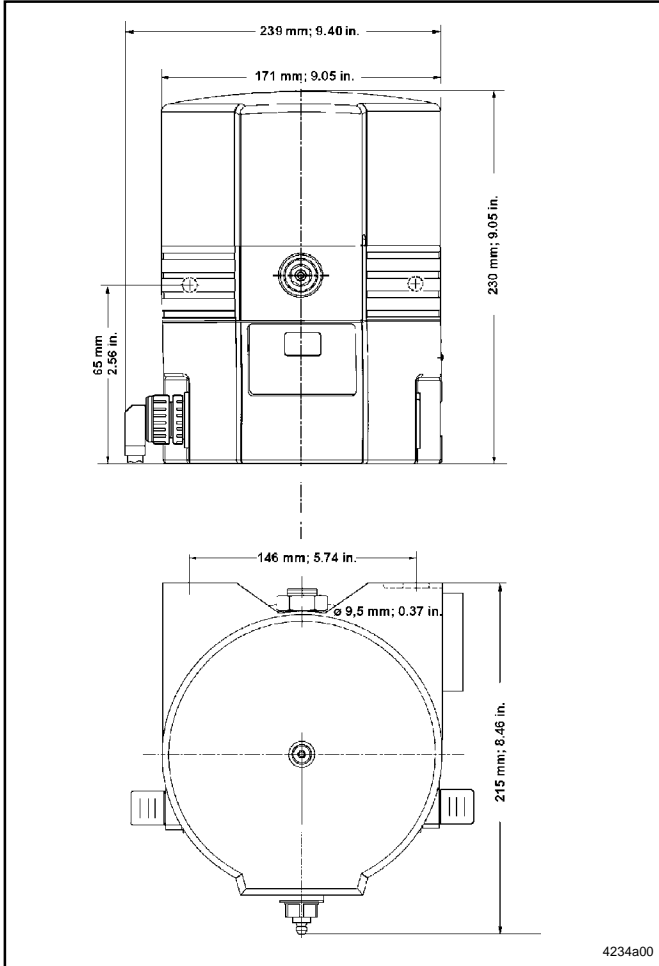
Cotes dimensionnelles de la pompe QLS 321
